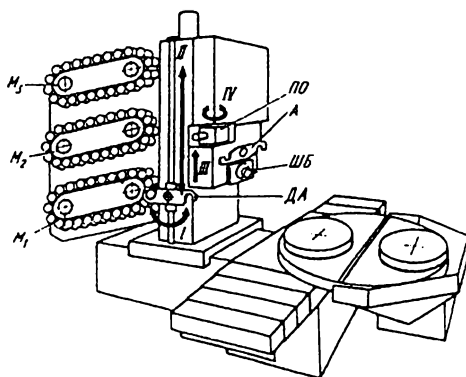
Компоновка верстата з горизонтальним шпинделем і трьома магазинами ланцюгового типу:
